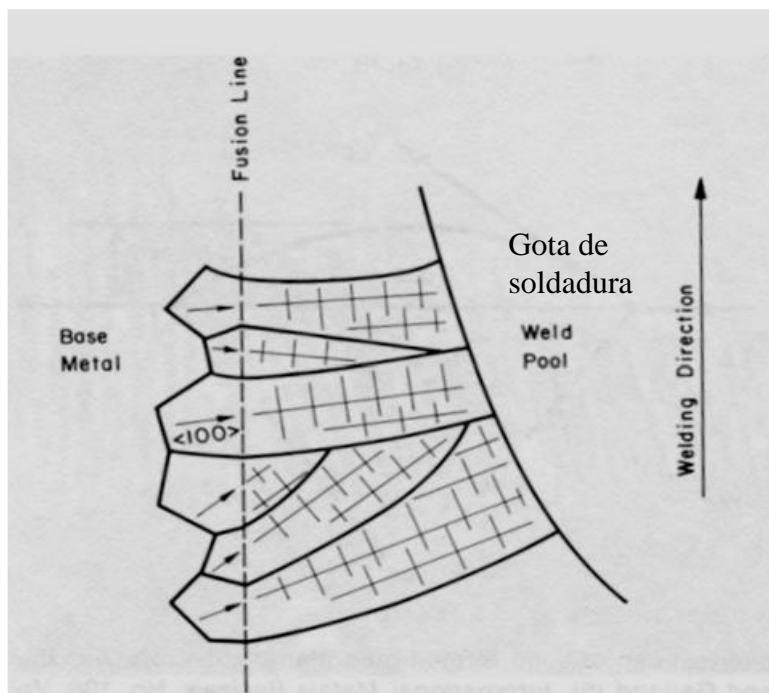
, Crecimiento epitaxial de la soldadura.
